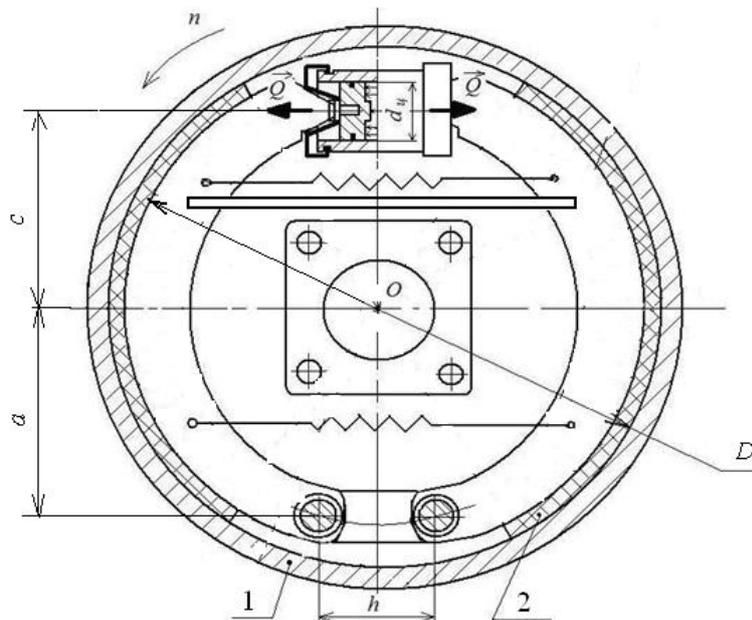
Схема конструкции заднего барабанного тормоза: тормозной барабан; 2 – колодки тормозные
